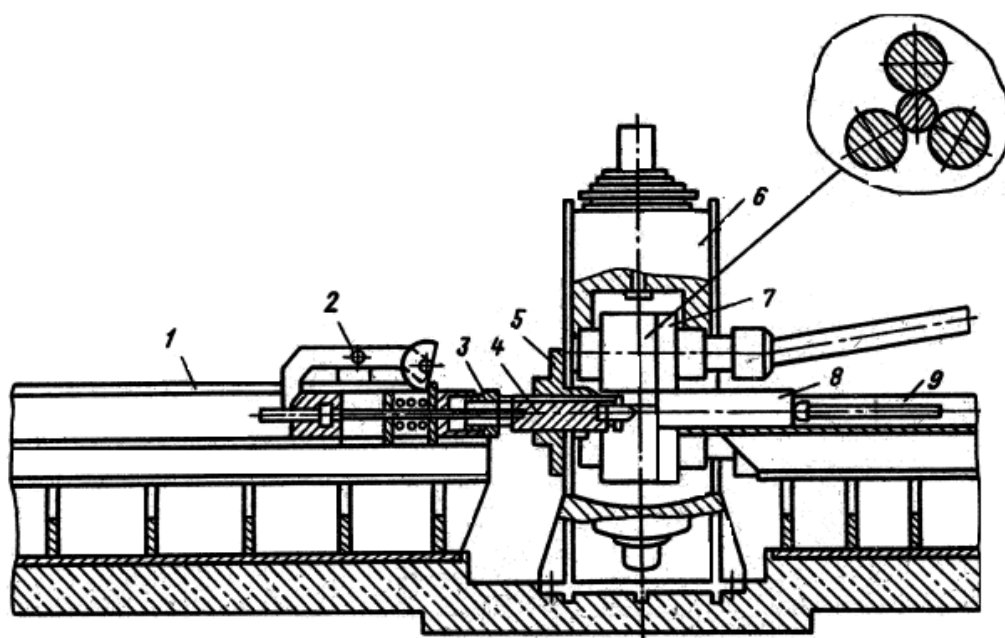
Устройство для зацентровки заготовки на базе опытно-промышленного стана
